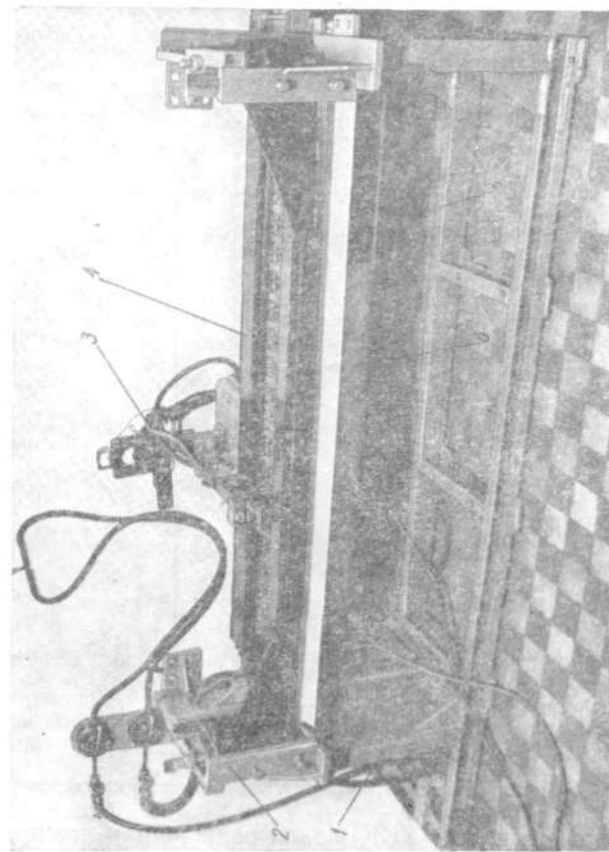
Установка для сварки продольных стыков обечаек (УСПО).
